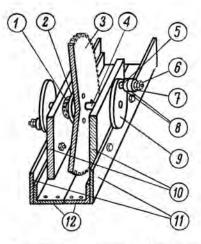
Узел кулисы в сборе: 1— шариковые подшинники 30×10 мм. (2 шт.); 2— фланец оси; 3— ведомая шестерня; 4— ось кулисы; 5— ось щечки; 6— гайка с контргайкой; 7— кулачок кулисы; 8— шариковые подшинники 22×8 мм (2 шт.); 9— щечка кулисы; 10— стойки кулисы; 11— накладки; 12— угловой дюралюминий (30×30 мм.).
